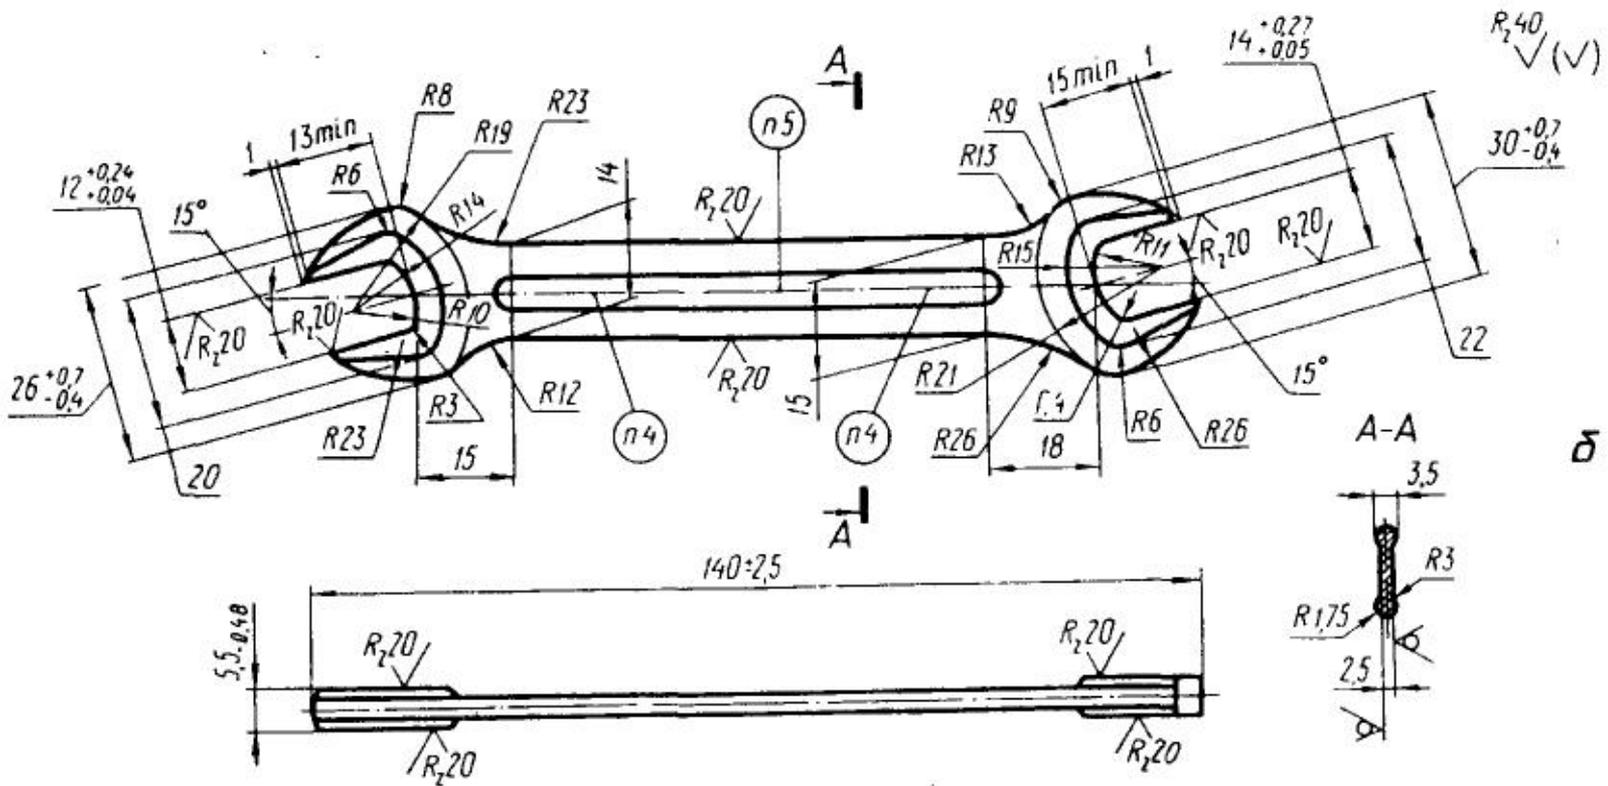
Креслення деталі, виготовленої гарячим штампуванням.
